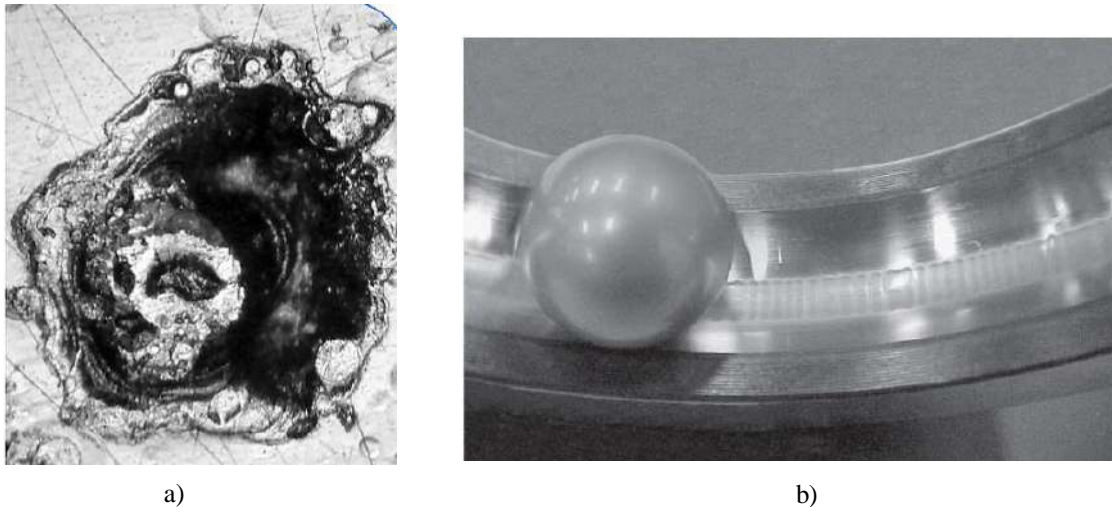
Daño en los rodamientos del motor, a)SKF picadura b)estriado (ABB).
